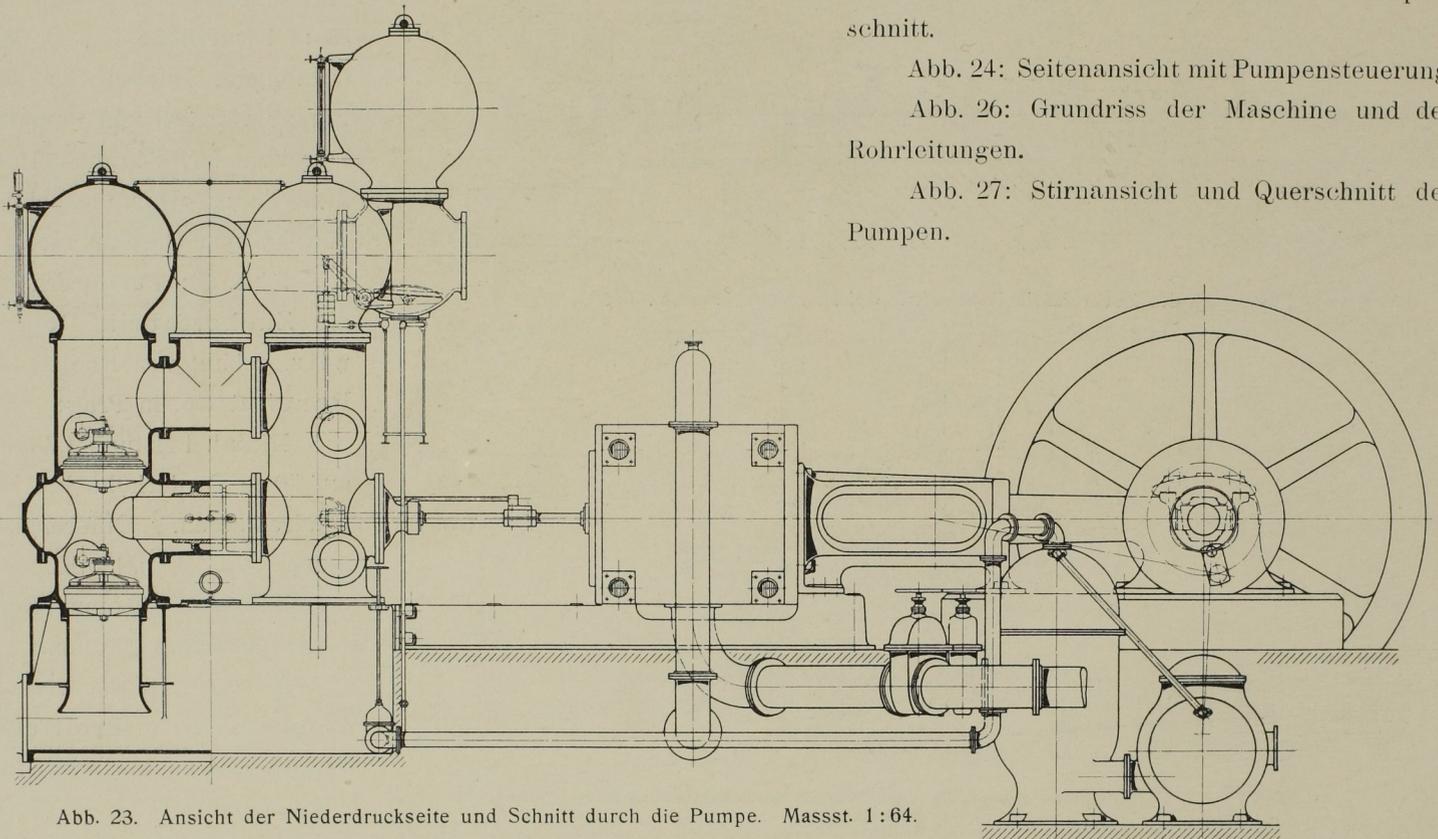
Ansicht der Niederdruckseite und Schnitt durch die Pumpe. Masst. 1:64.
